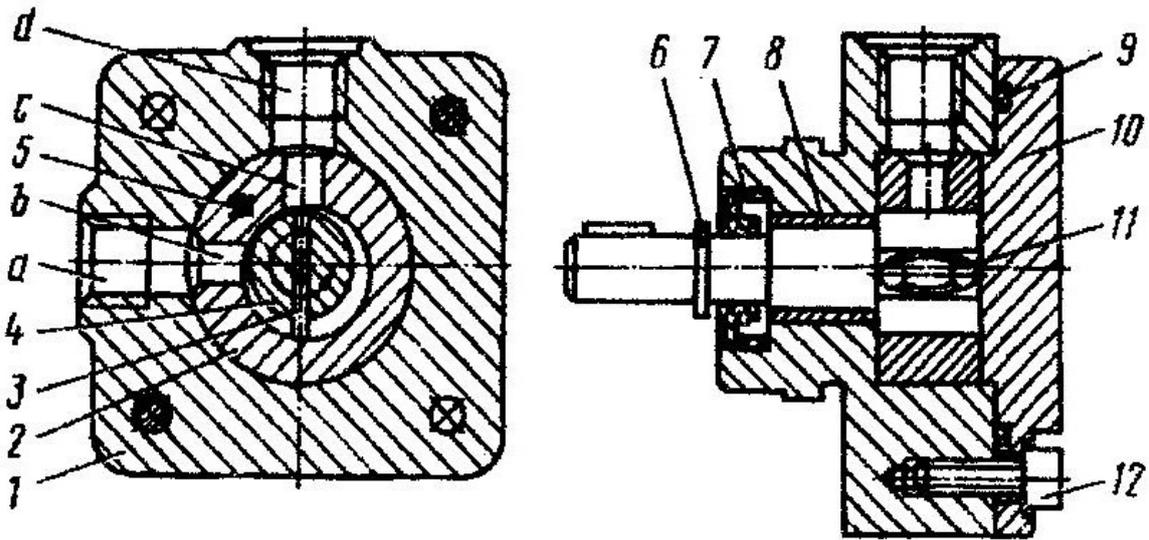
Насос пластинчатый для смазки типа С12-5М:
